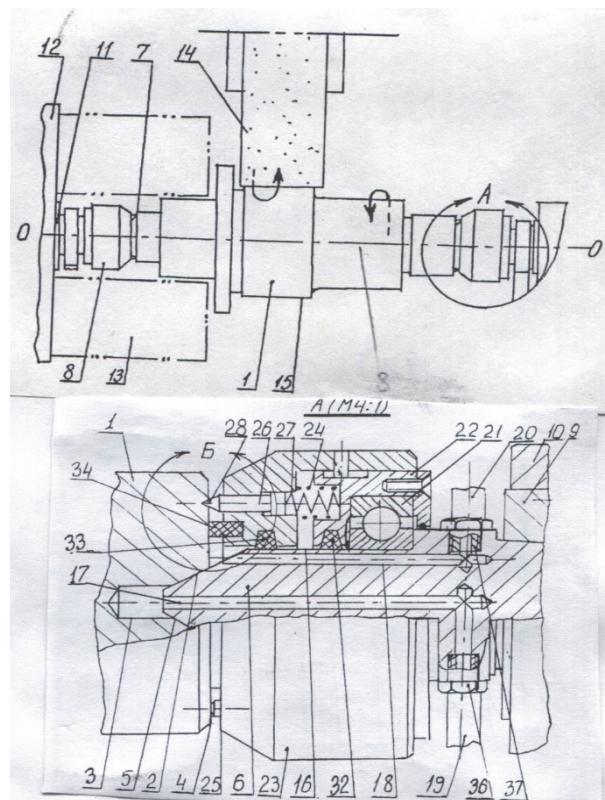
Схема способа установки заготовки (пат. 2168395) по оси симметрии
